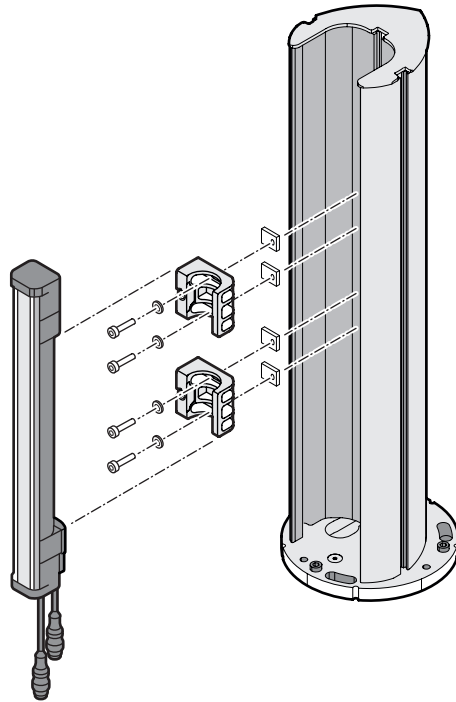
Montage de la fixation FlexFix sur une colonne (accessoire)
